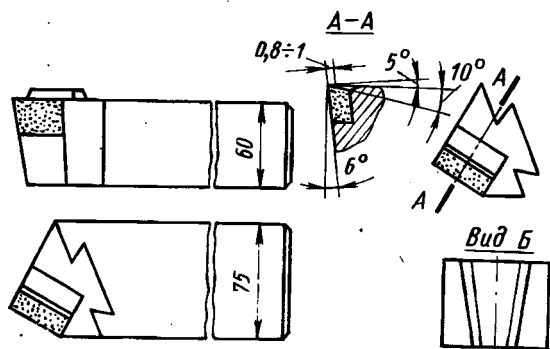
Проходной правый резец с клиновым креплением вкладыша
